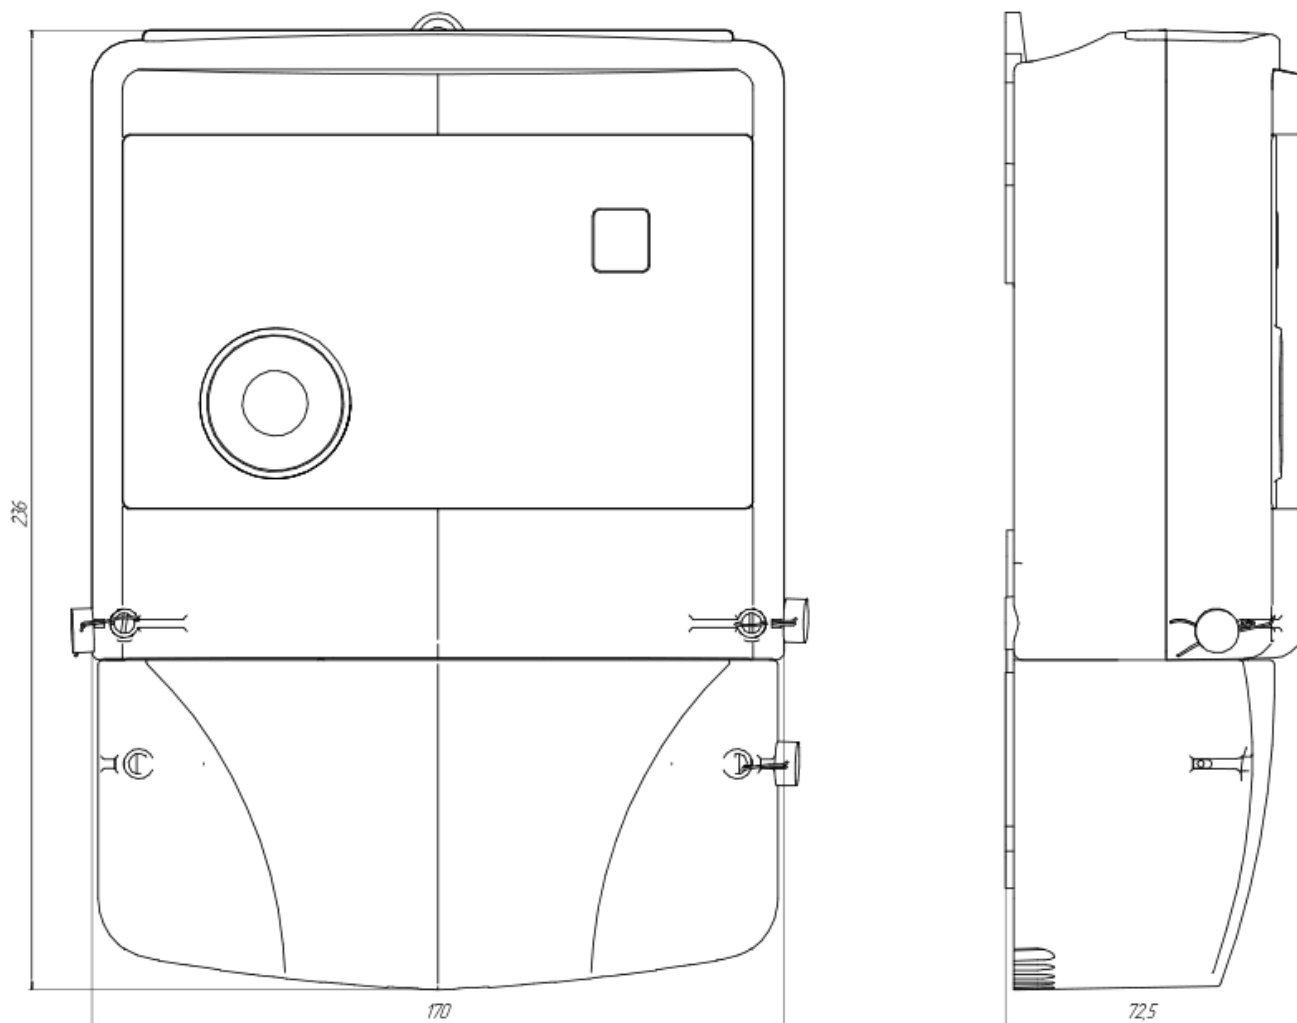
Габаритный чертеж и установочные размеры счетчика.
